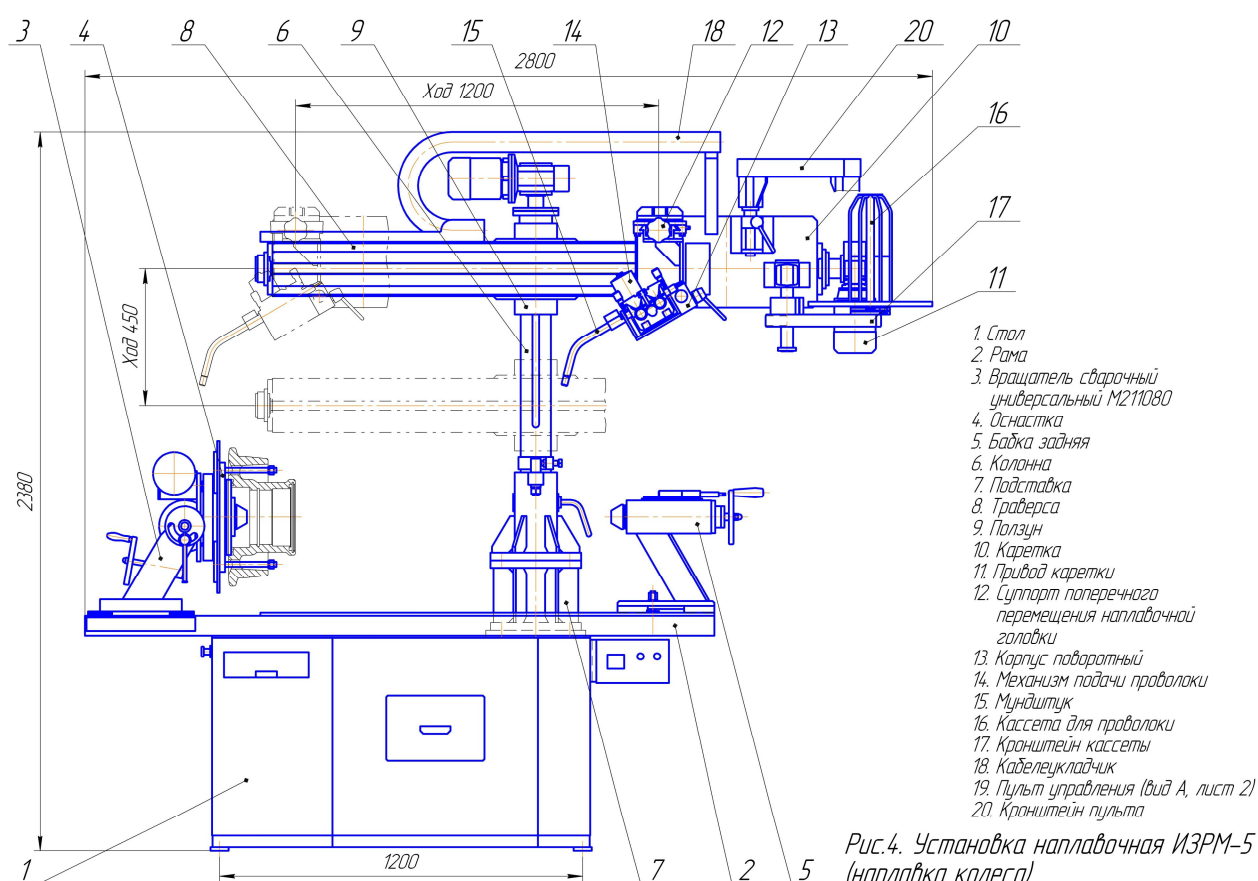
Установка наплавочная ИЗРМ-5 (наплавка колеса)
